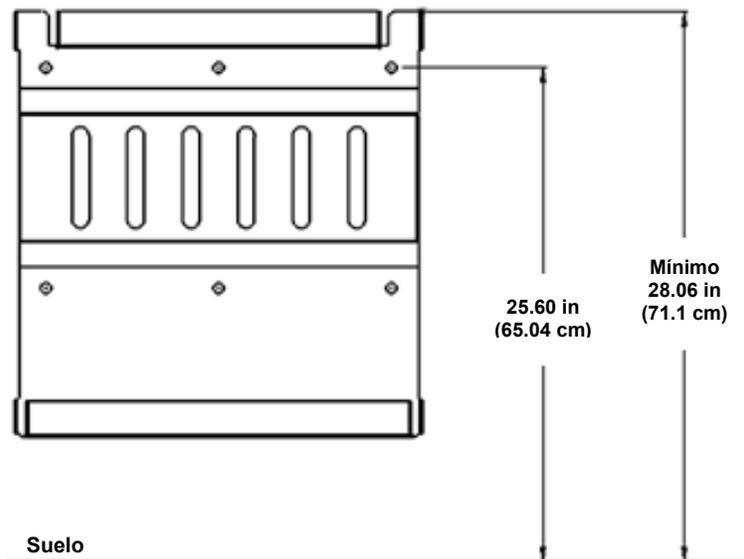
WallMount Instalación Con Caja de Conducto Pasos 1 y 2
